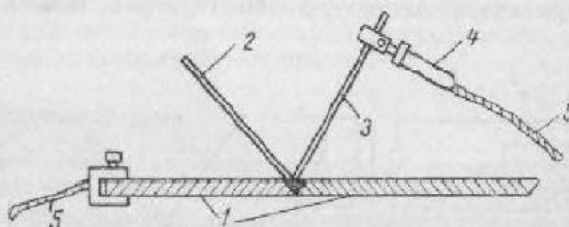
Схема сварки по методу Бенардоса.
